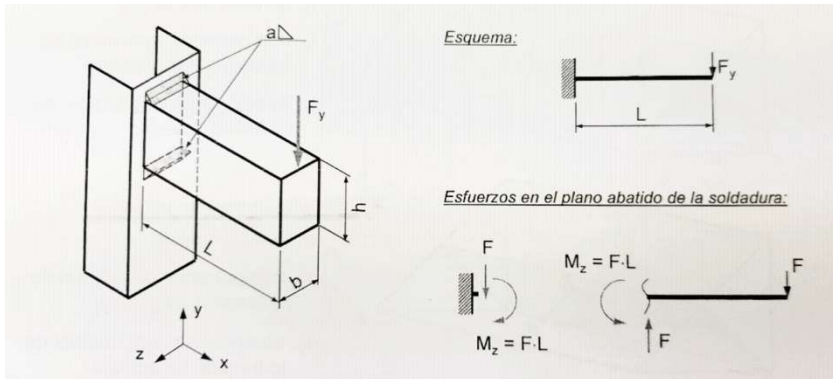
Soldadura travesaños 1 y 3 con larguero.
